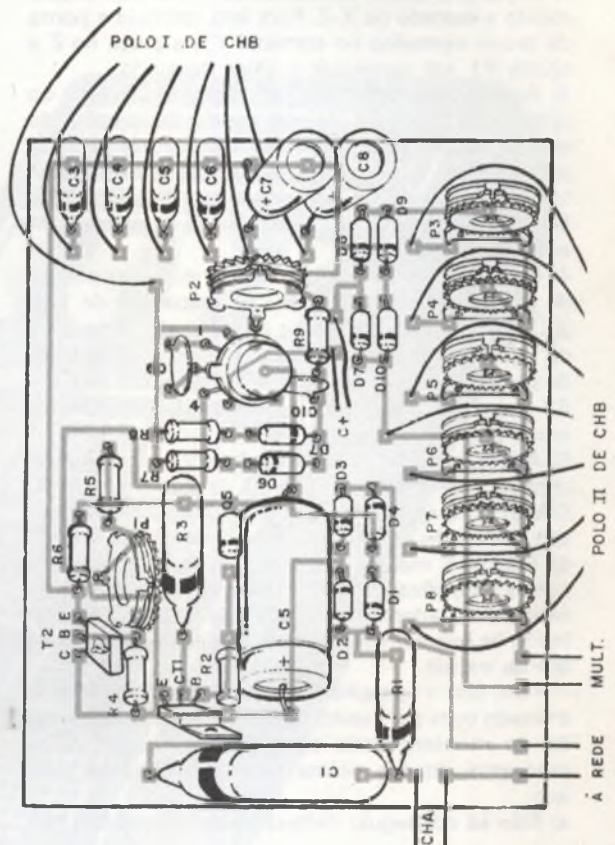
B- Placa de Circuito Impresso vista pelo lado dos componentes.
